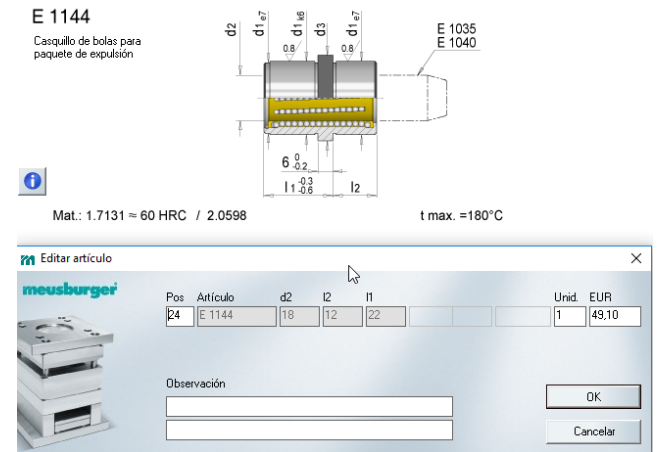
19 Casquillo de bolas para paquete de expulsión.
